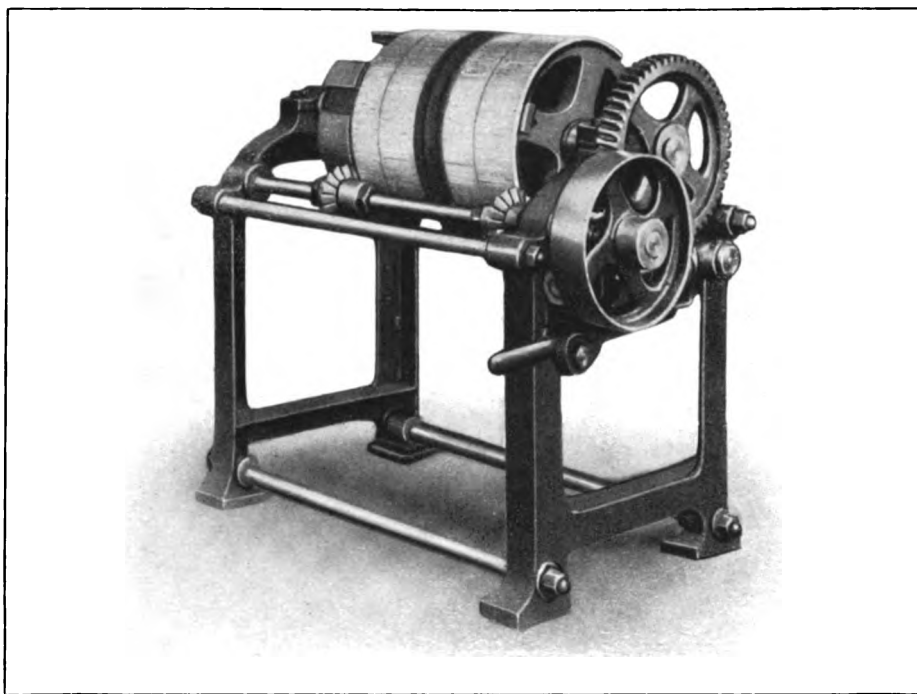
SELBSTTÄTIGE FRASEMASCHINE NUR ZUM BEARBEITEN
